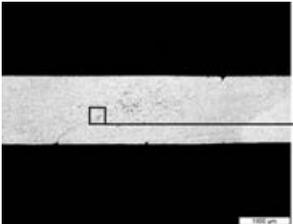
Rollennahtschweißung, Quetschnaht: DC06, Bandanbindung, Inspektionslinie; Dicke 1,2 mm, Schweißung mit geringerer Überlappung; keine oder geringe Nahtüberhöhung.
